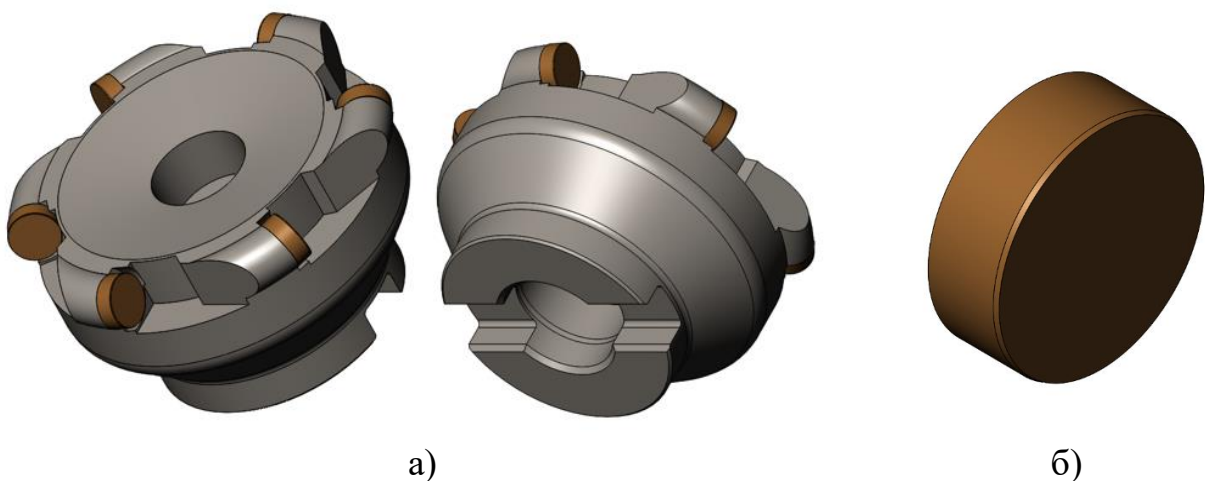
Тривимірні моделі стандартної фрези Seco Tools R220.70-0063-09-6
